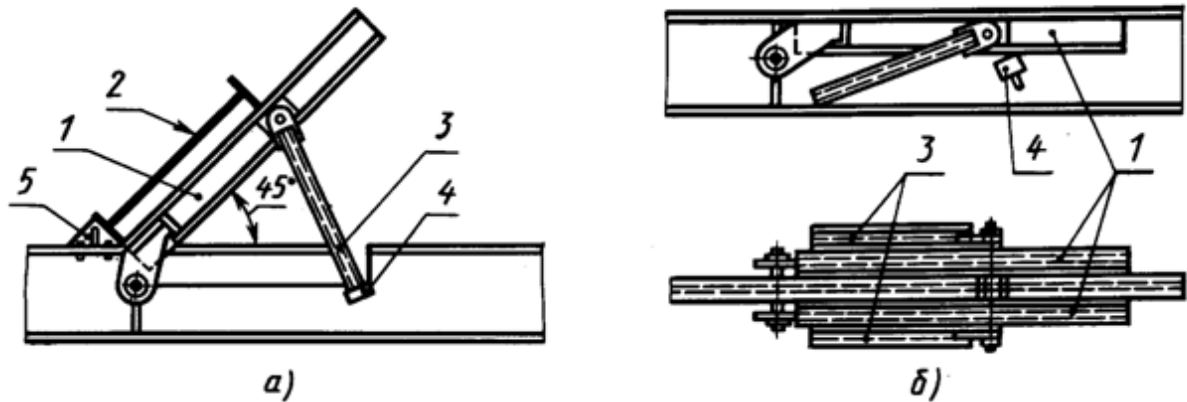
Пристрій для встановлення балок під зварювання
